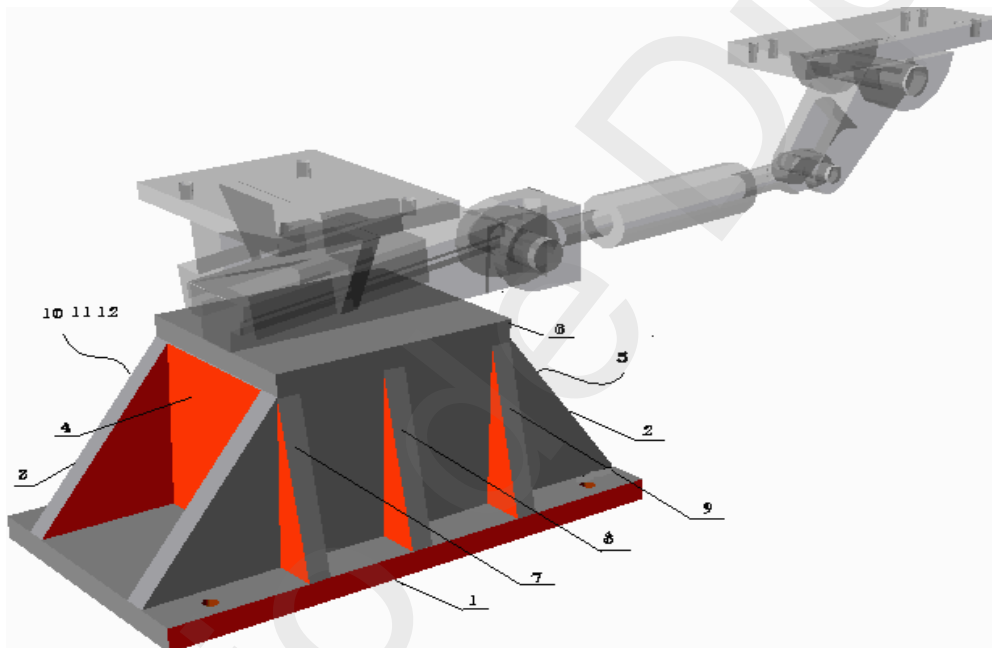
Elementos de la base del mecanismo de apoyo.
